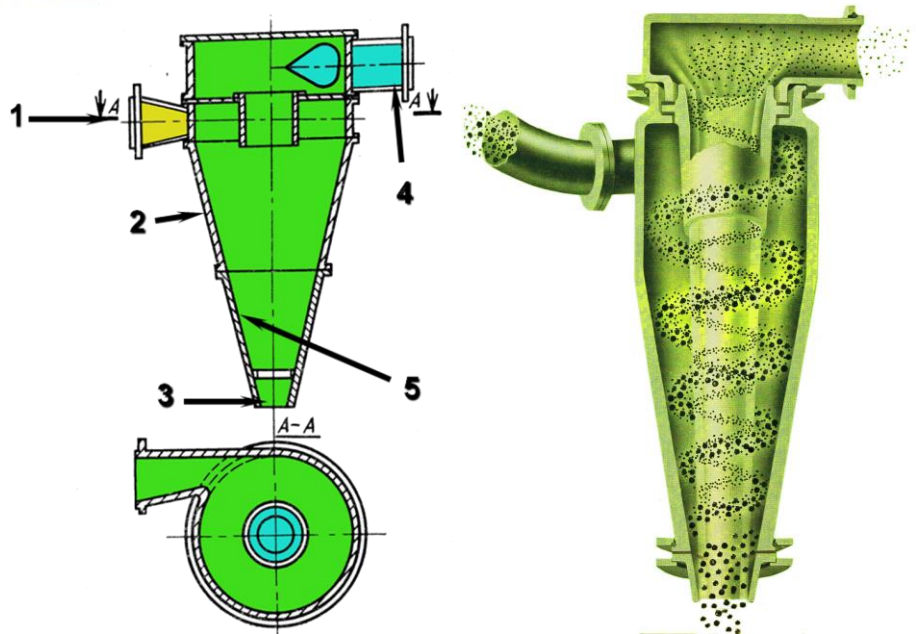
Гидроциклон: 1 – подача питания; 2 – корпус; 3 – песковая насадка; 4 – сливной патрубок; 5 – футеровка
